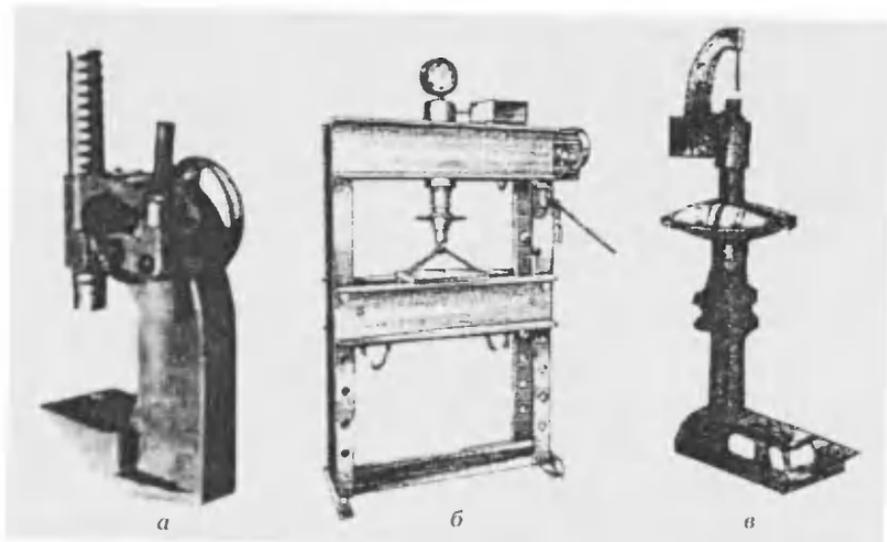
Различные прессы для разборочно-сборочных работ: *а* — электрогидравлический напольный пресс 2135-1М с дополнительным плунжерным насосом и ручным приводом для разборки и сборки мелких узлов, *б* — пневматический напольный пресс Р-304 для клепки фрикционных накладок, *в* — настольный пресс ОКС-918 с ременным приводом
